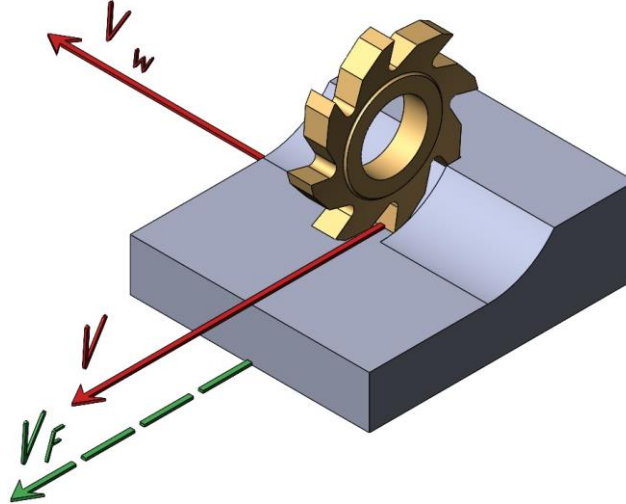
Высокоскоростное плунжерное фрезерование дисковой фрезой
